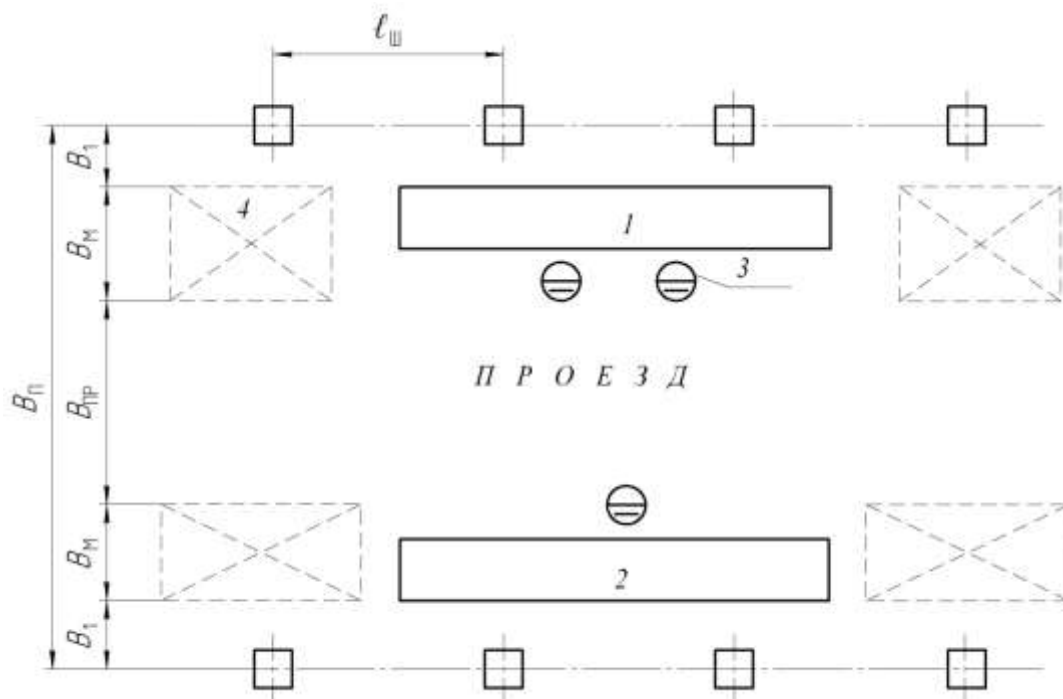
Схема планировки цеха при расположении складочных мест поперек ряда (между оборудованием): 1 – сборочно-сварочный стеллаж; 2 – сборочно-сварочный стенд 3 – рабочее место; 4 – складочное место
